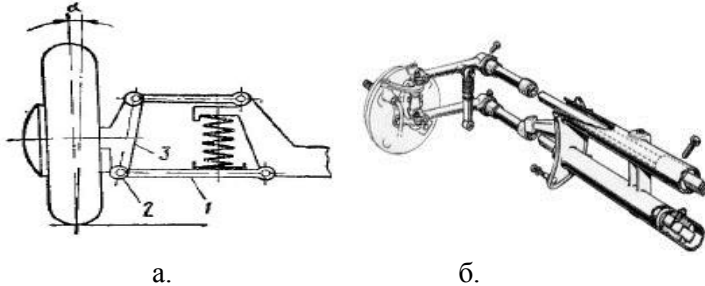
Схеми підвісок з металевими пружними елементами (а- пружиною; б- торсіоном).
